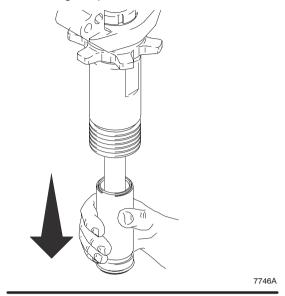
Retourner la tige de piston et la chemise et les heurter contre une surface dure jusqu'à ce que la tige de piston sorte de la chemise.
